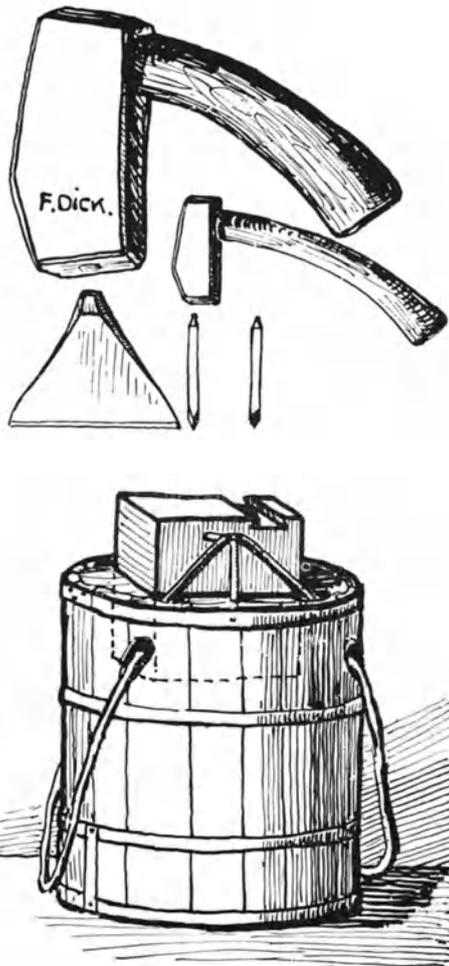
Die wichtigsten Werkzeuge eines Handhauers.
